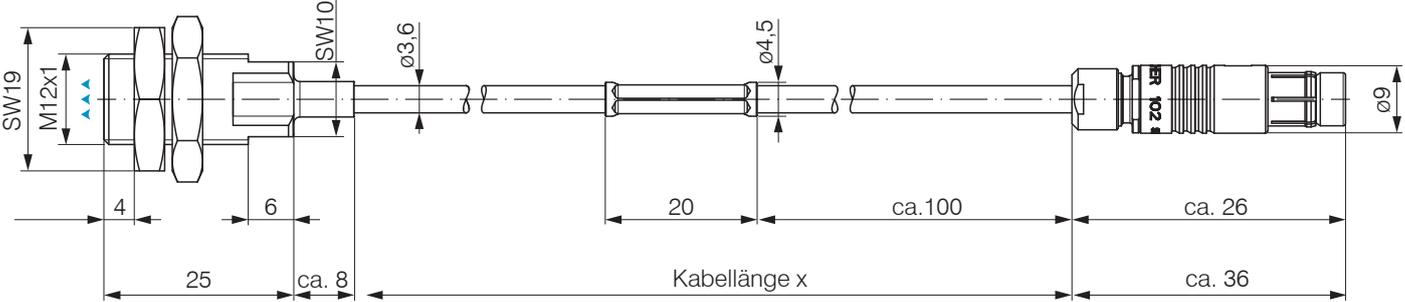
Maßzeichnung Sensoren ES-S2-C-CAX/mB0, Abmessung in mm
